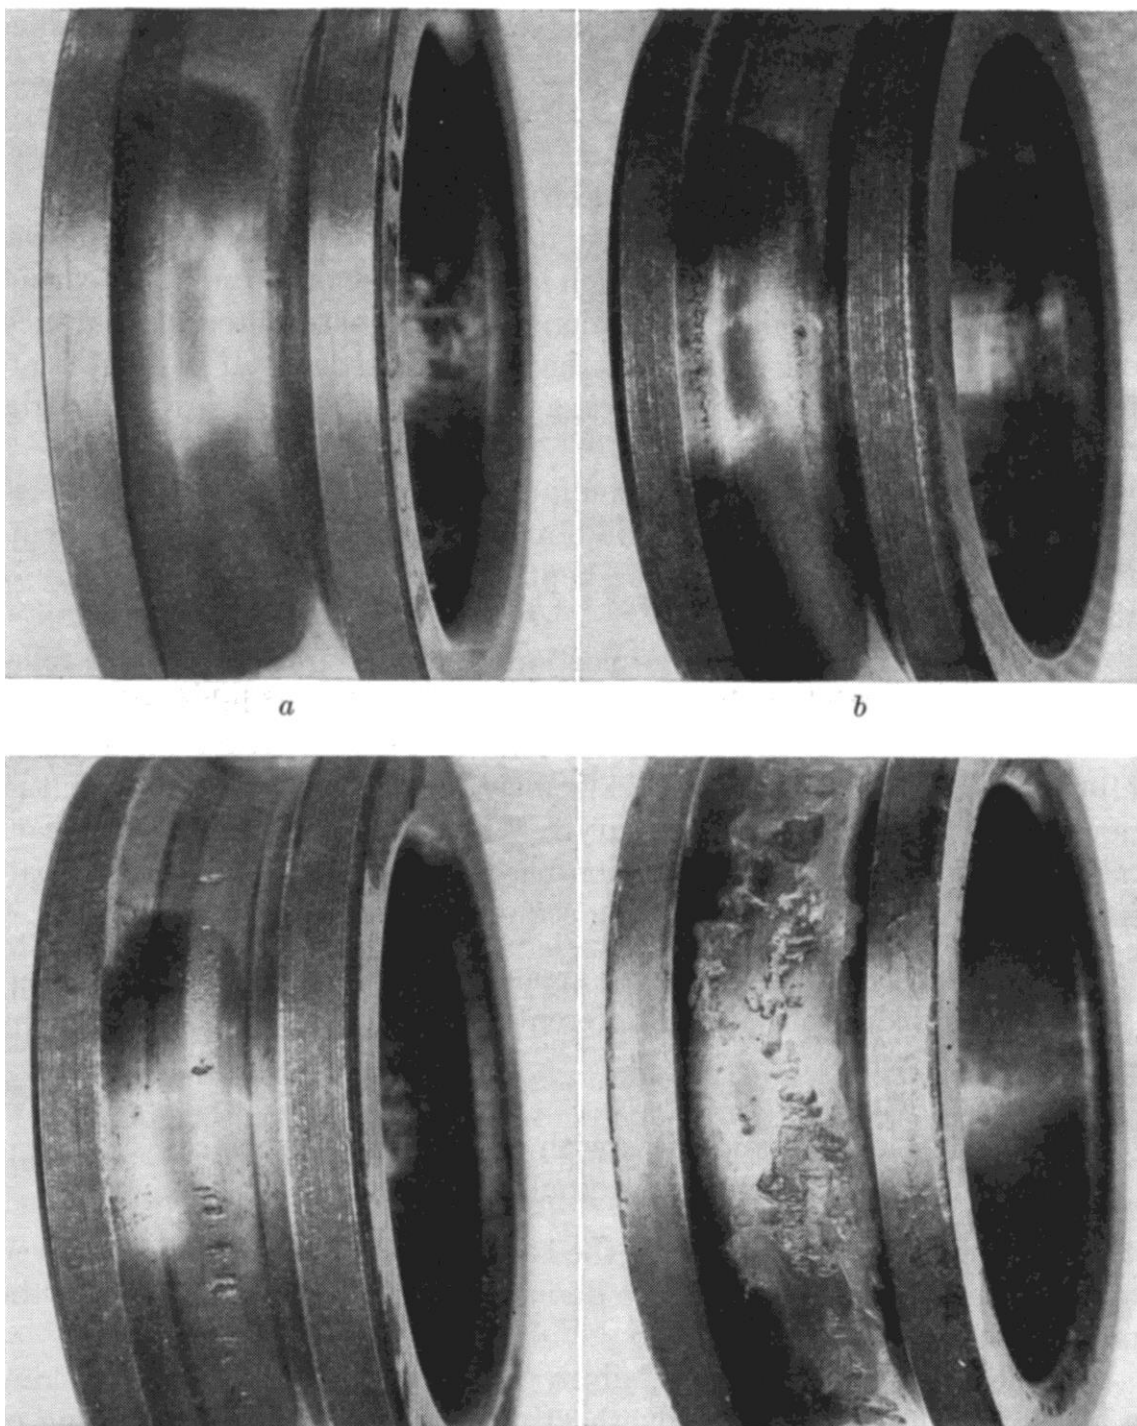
vistas de la progresión de avería por falta o escasez de lubricante [1].
